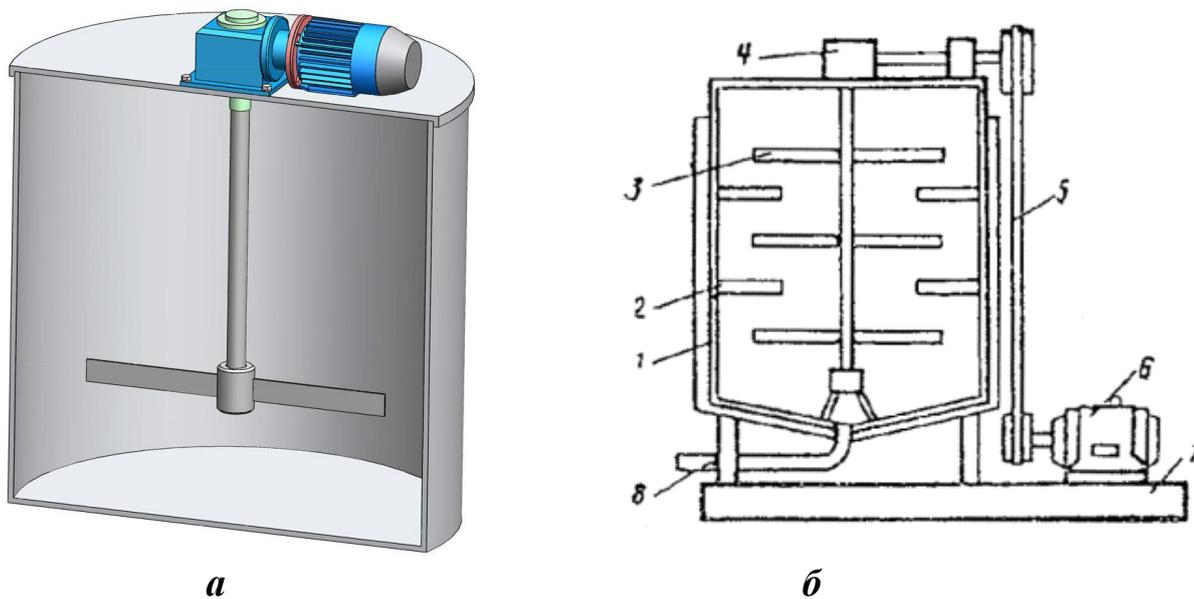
Разрез (а) и схематическое изображение (б) лопастной мешалки для приготовления обратных эмульсий: 1 – корпус; 2 – неподвижная лопасть; 3 – подвижная лопасть; 4 – шестеренчатая передача; 5 – ременная передача; 6 – электродвигатель; 7 – рама; 8 – сливной патрубок
